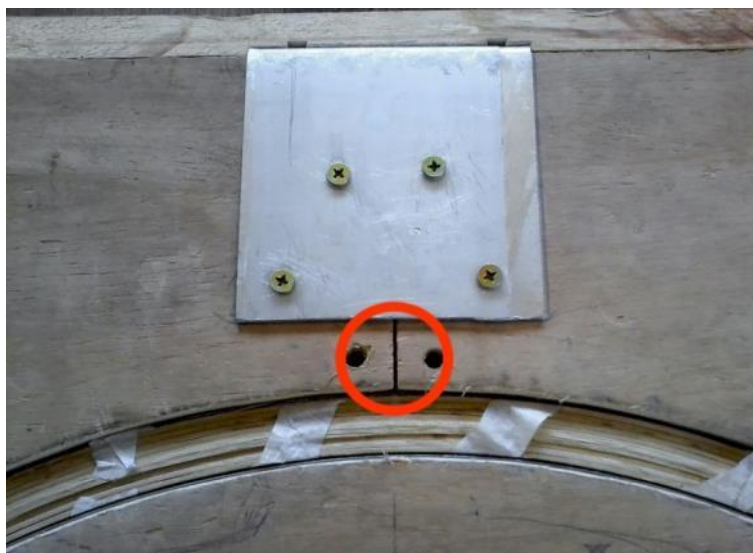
Peças para fixar as duas partes do molde e o molde sendo testado.
